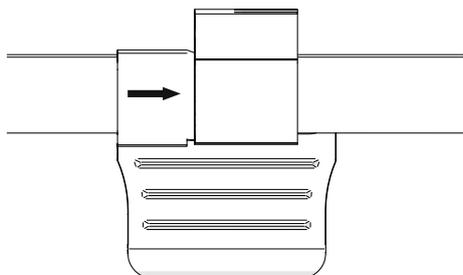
Demontage-Werkzeug in der Anwendung (seitlich)
